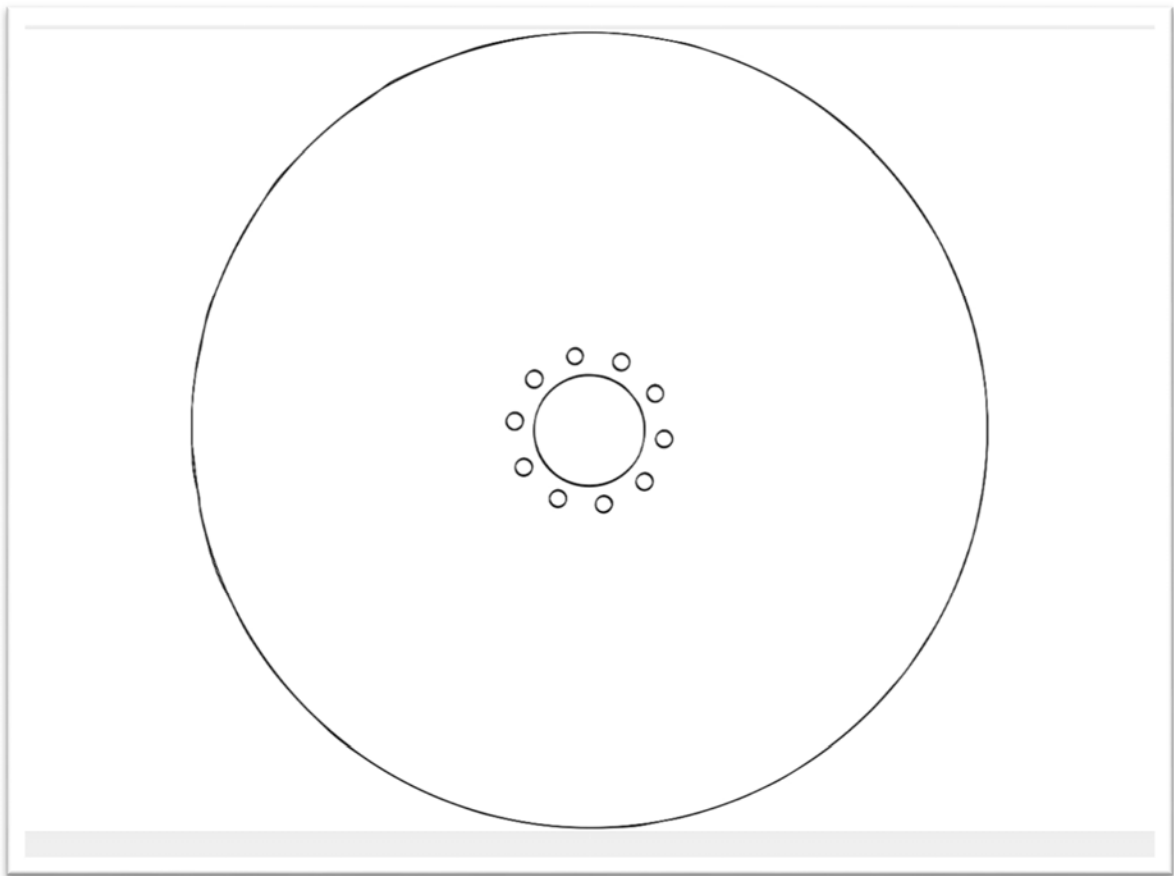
Aproximación zona central de la primera sección (Fotogrametría)
